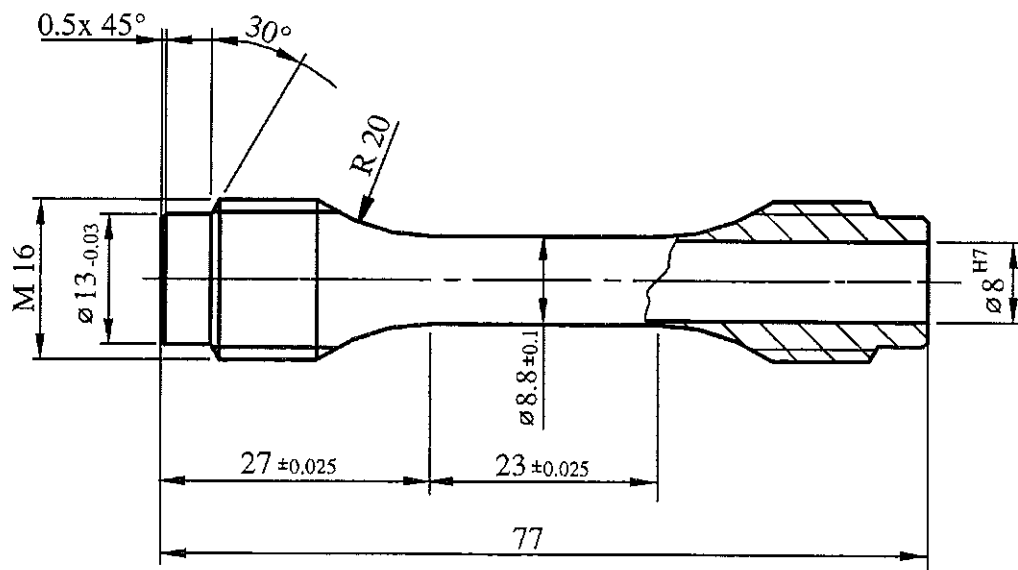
Zylindrische Hohlproben für das Einstab-Prüfsystem (Probenform C).
